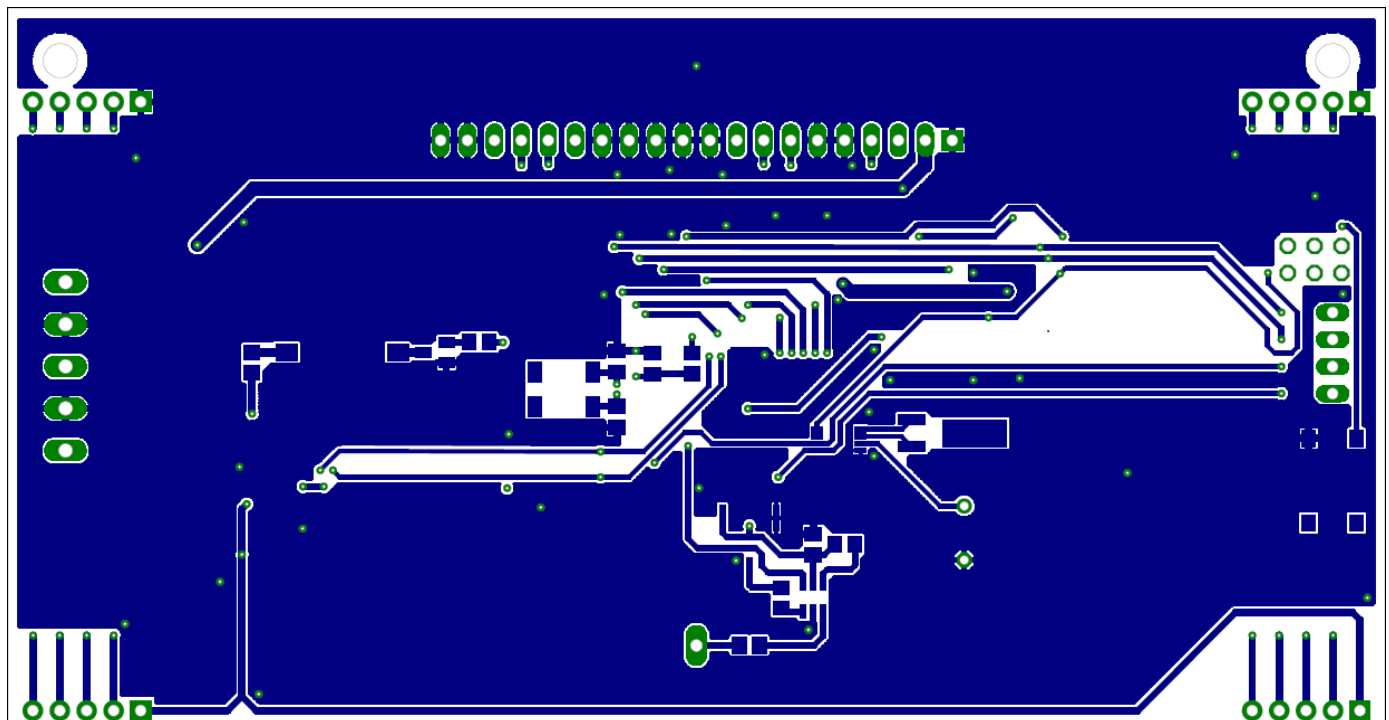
Layout BasisPCB gespiegelt Bottom
